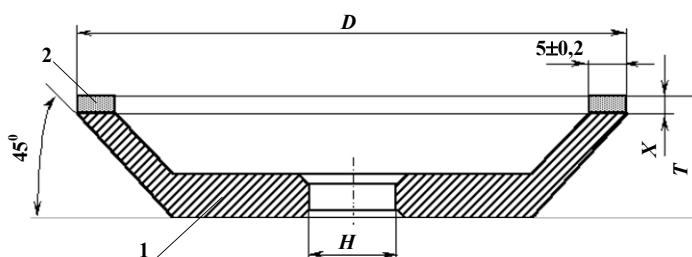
Схема шліфувального круга форми 12А2-45°: 1 – корпус; 2 – кубонітовий робочий шар
